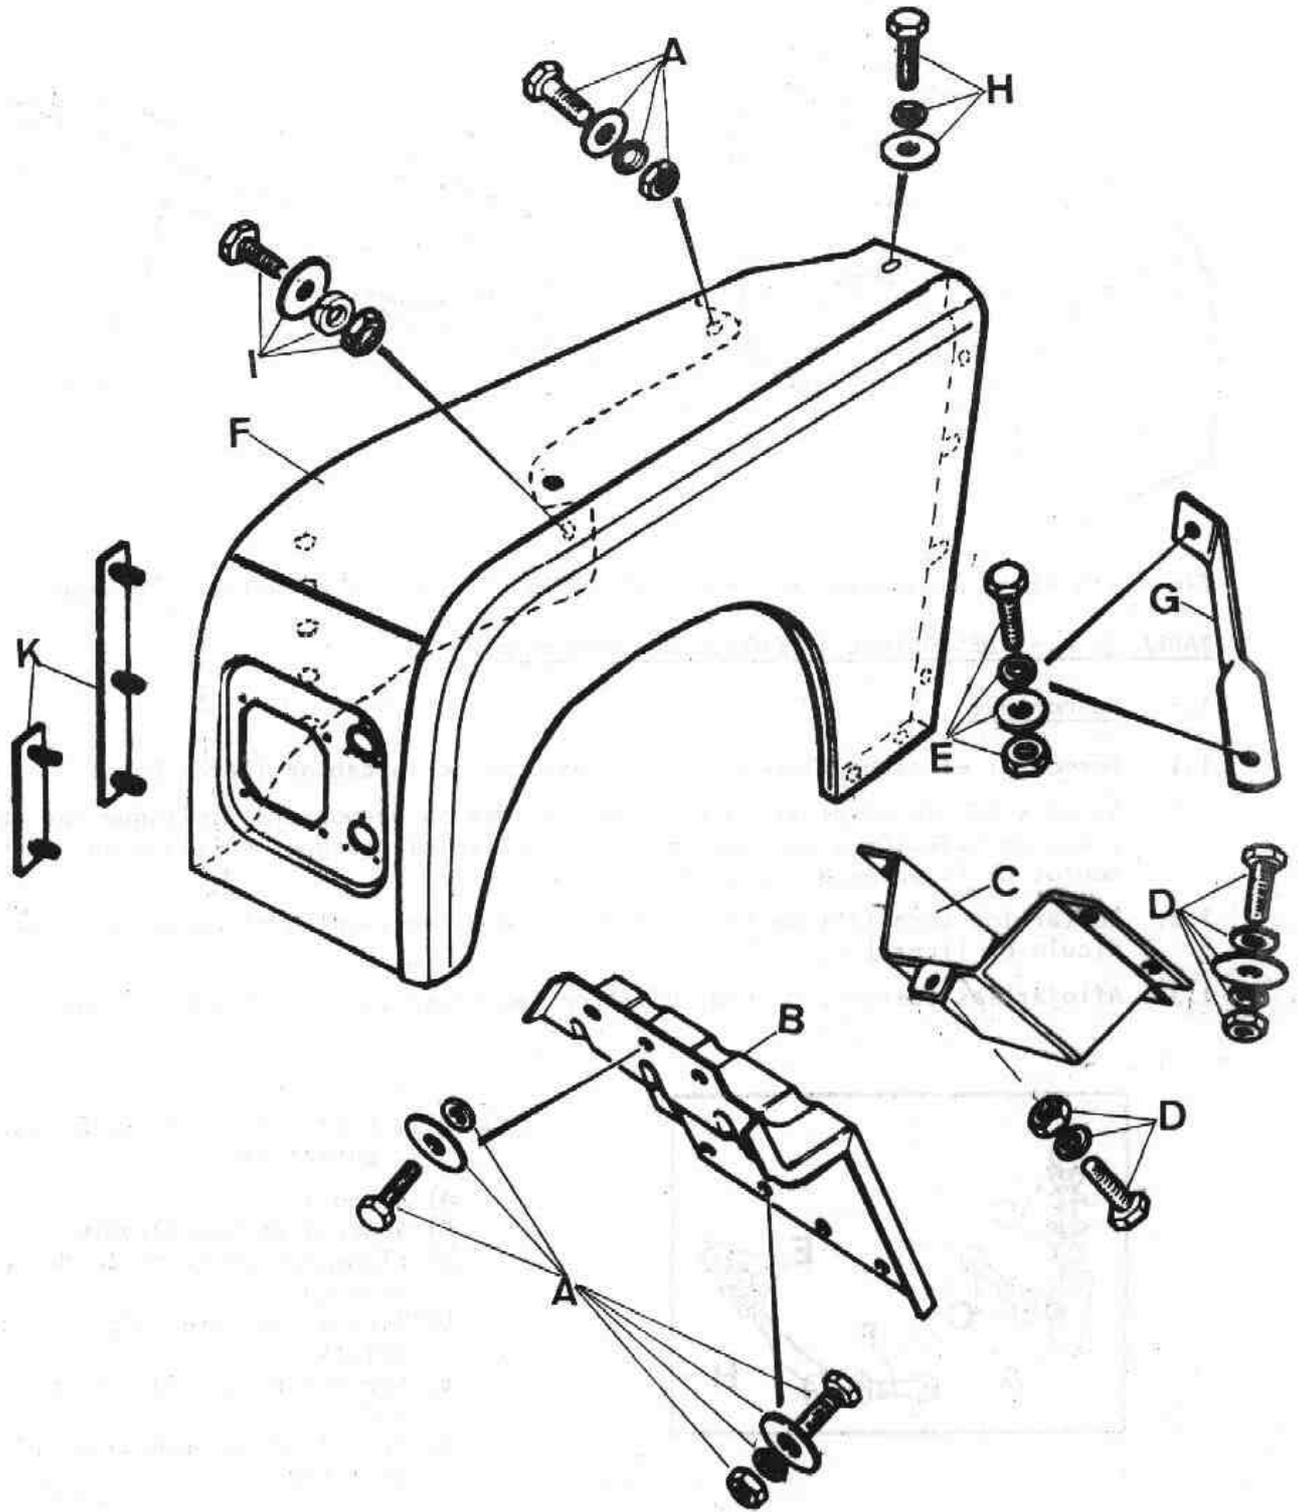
Desmontaje de la aleta (4 cilindros)
